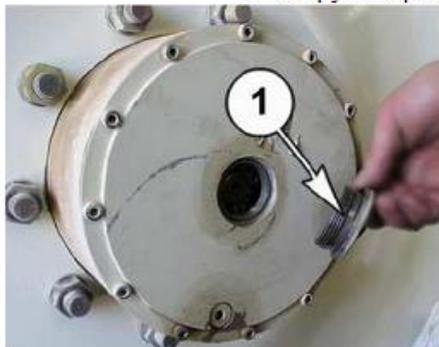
Отсоединение гидромотора от бортового редуктора.
